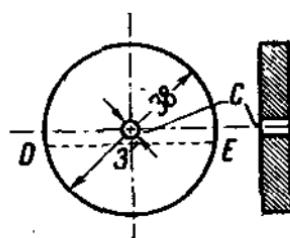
Заготовка шпонки Вудруфа с отверстием для шаблона.
